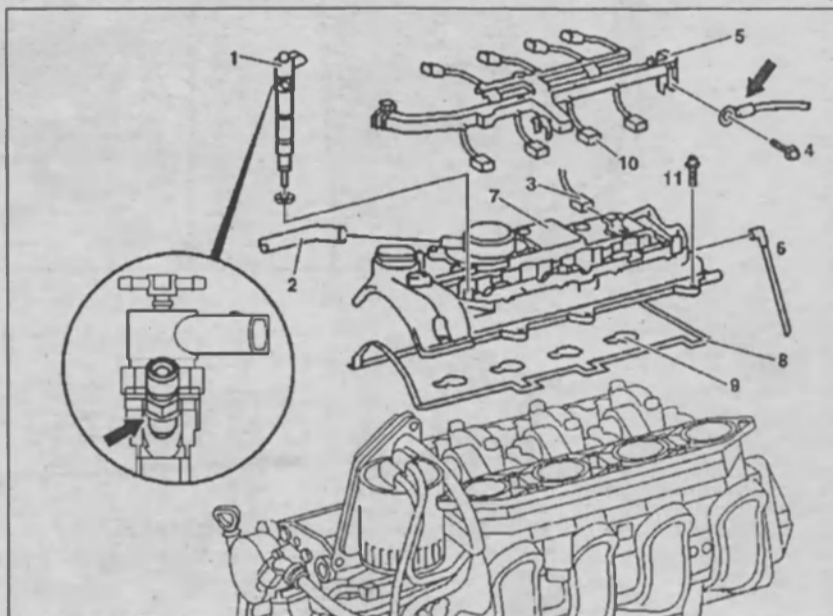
а. Снятие и установка крышки головки блока цилиндров на двигателях 611.981/983/987:
